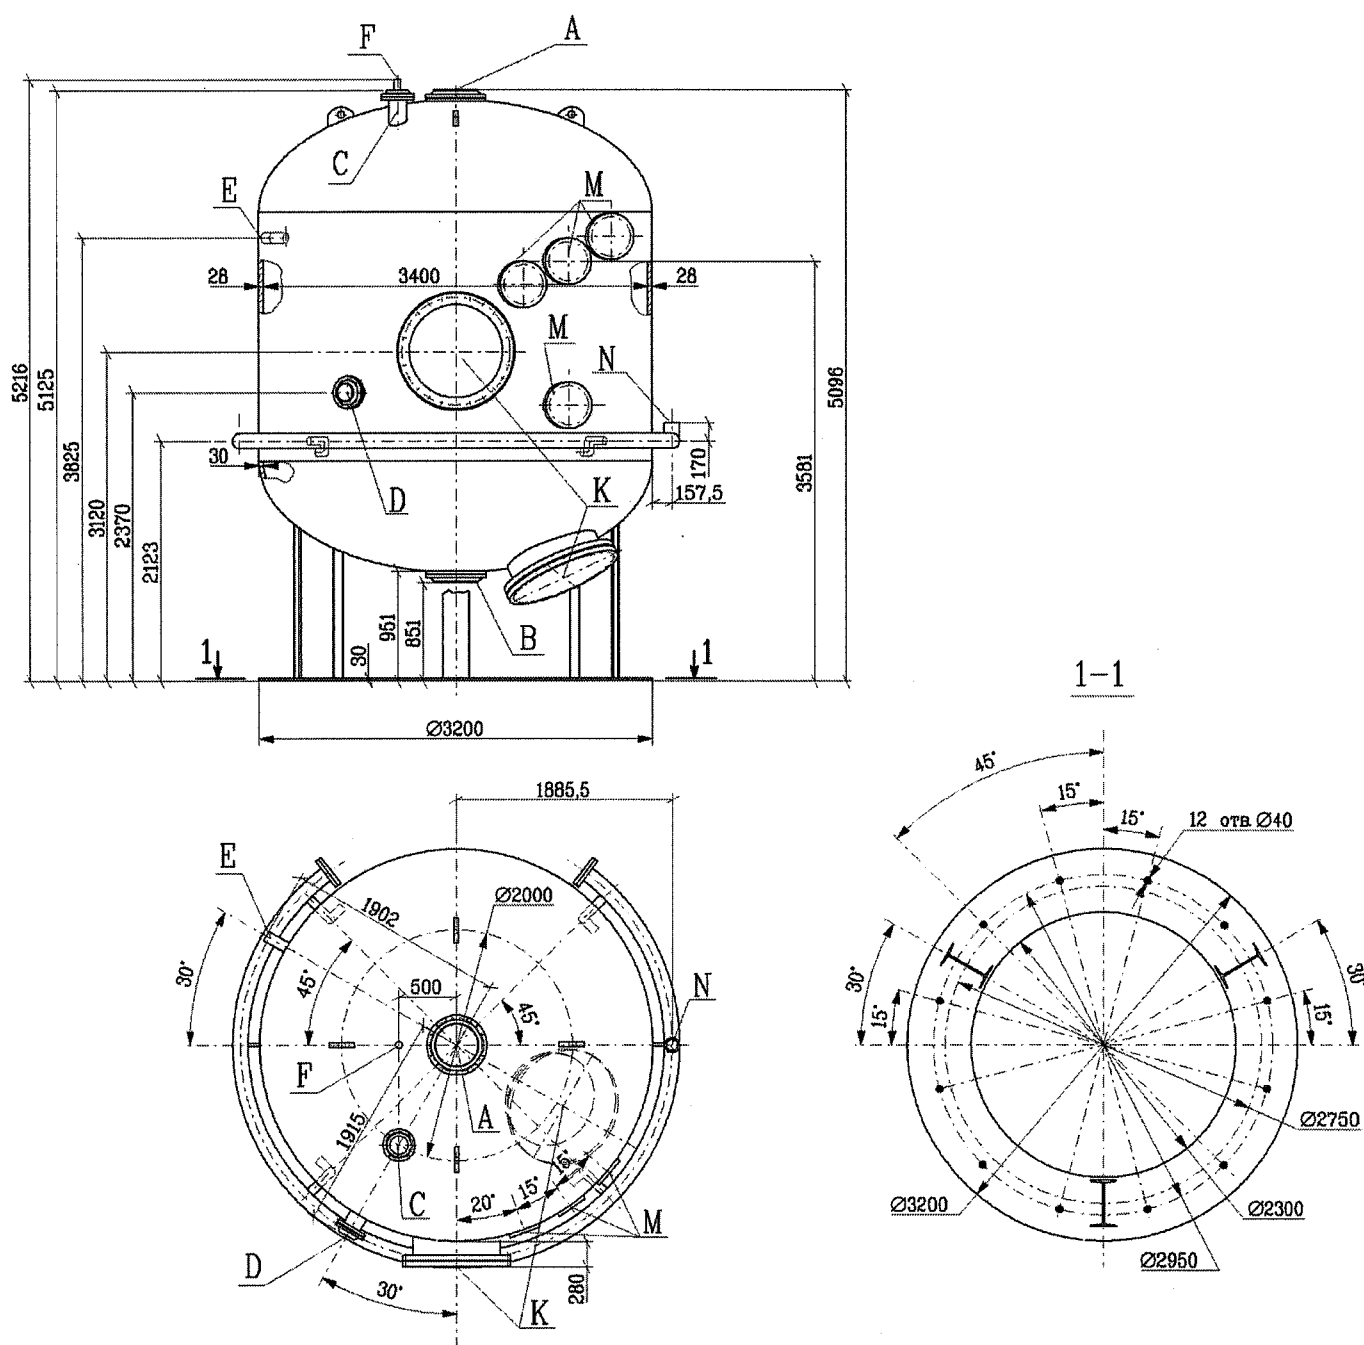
Габаритный чертеж фильтра Н-катионитного обезжелезивающего
